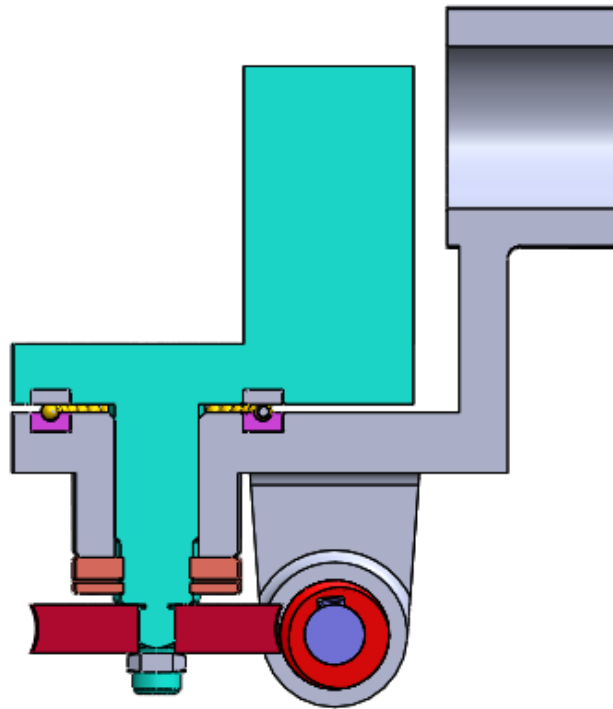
Приспособление для обработки шаровой поверхности (разрез)
